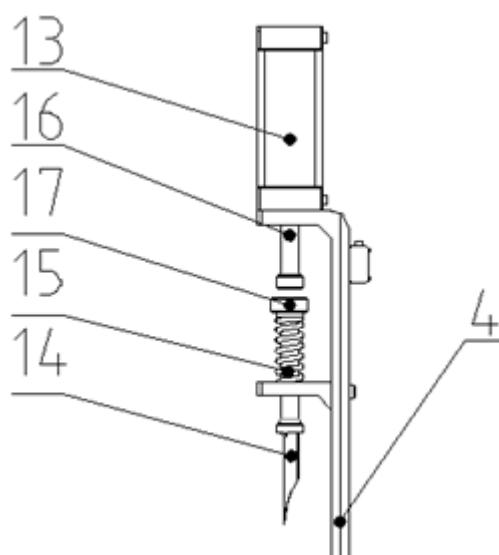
соединение пневмоцилиндра и фигурного ножа, вид слева
